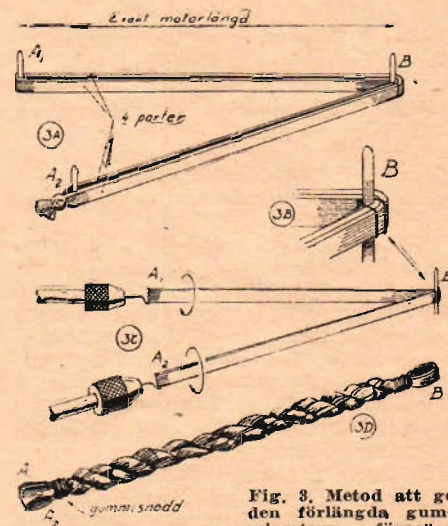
Metod att ge den förlängda gummimotorn förspänning.
